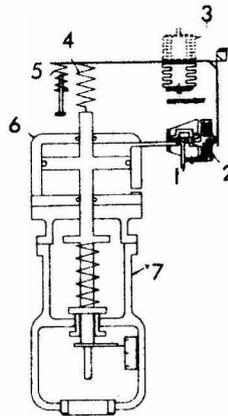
Partes Principales del Actuador Neumático de Pistón.
